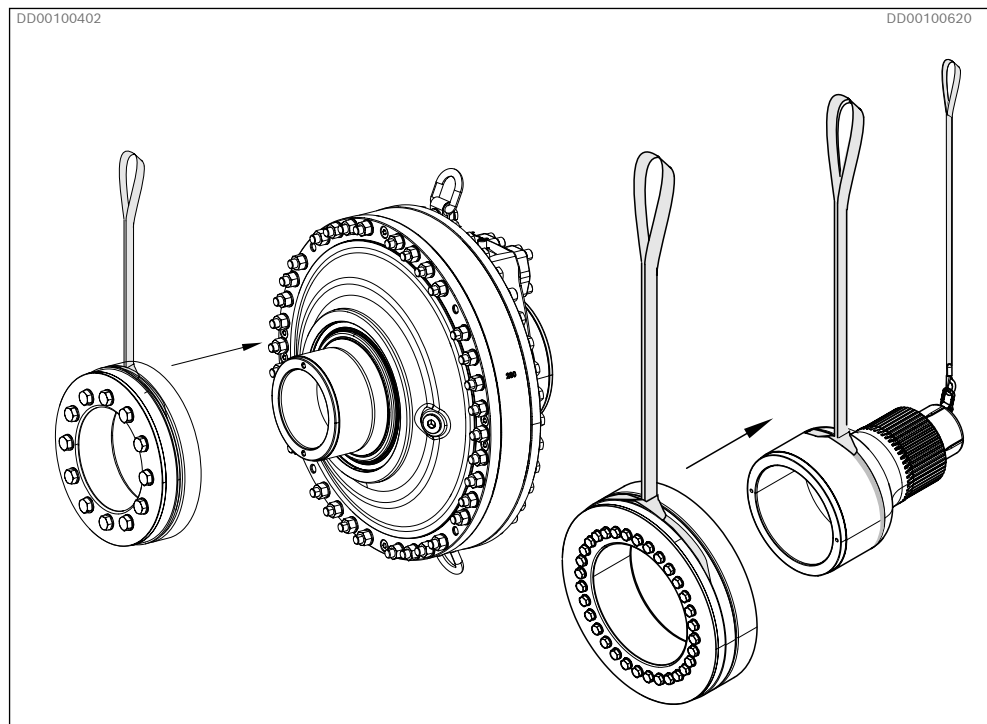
Монтаж стяжной муфты на адаптер вала или мотор, оснащенный муфтой
